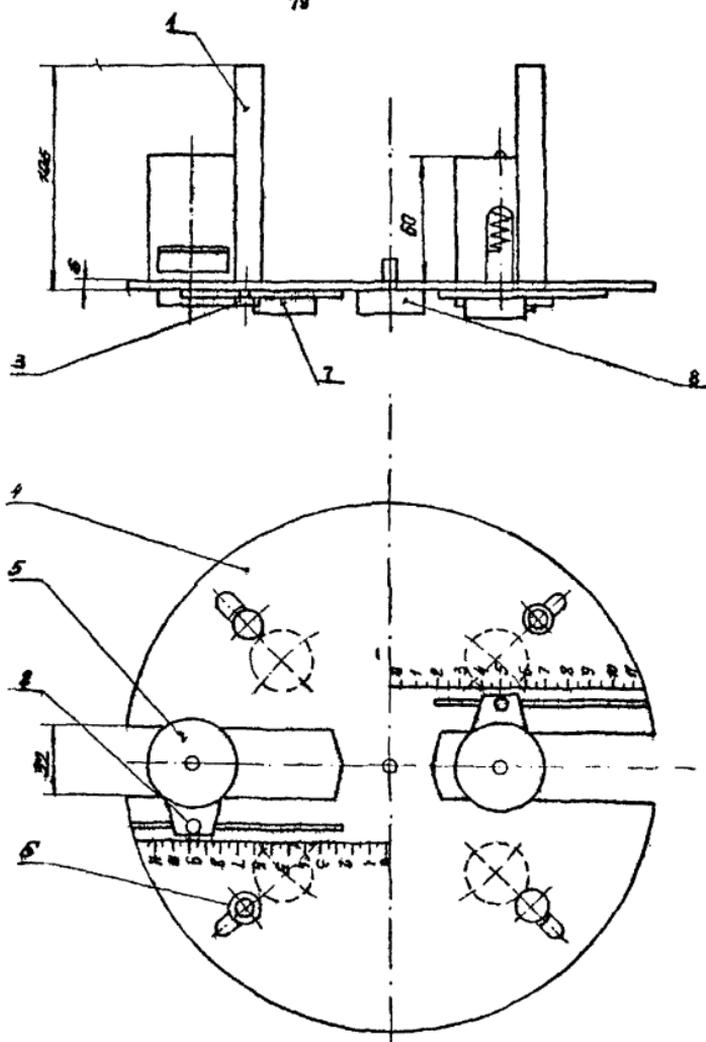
Приспособление для контроля осей копровых шкивов: 1 - ручка (2шт); 2 - фиксирующий винт (2шт); 3 - болт (2шт); 4 - основание; 5 - стаканы для искателя (2шт); 6 - гайка-барашек (2шт); 7 - магнит с линейкой (4шт); 8 - центратор.
